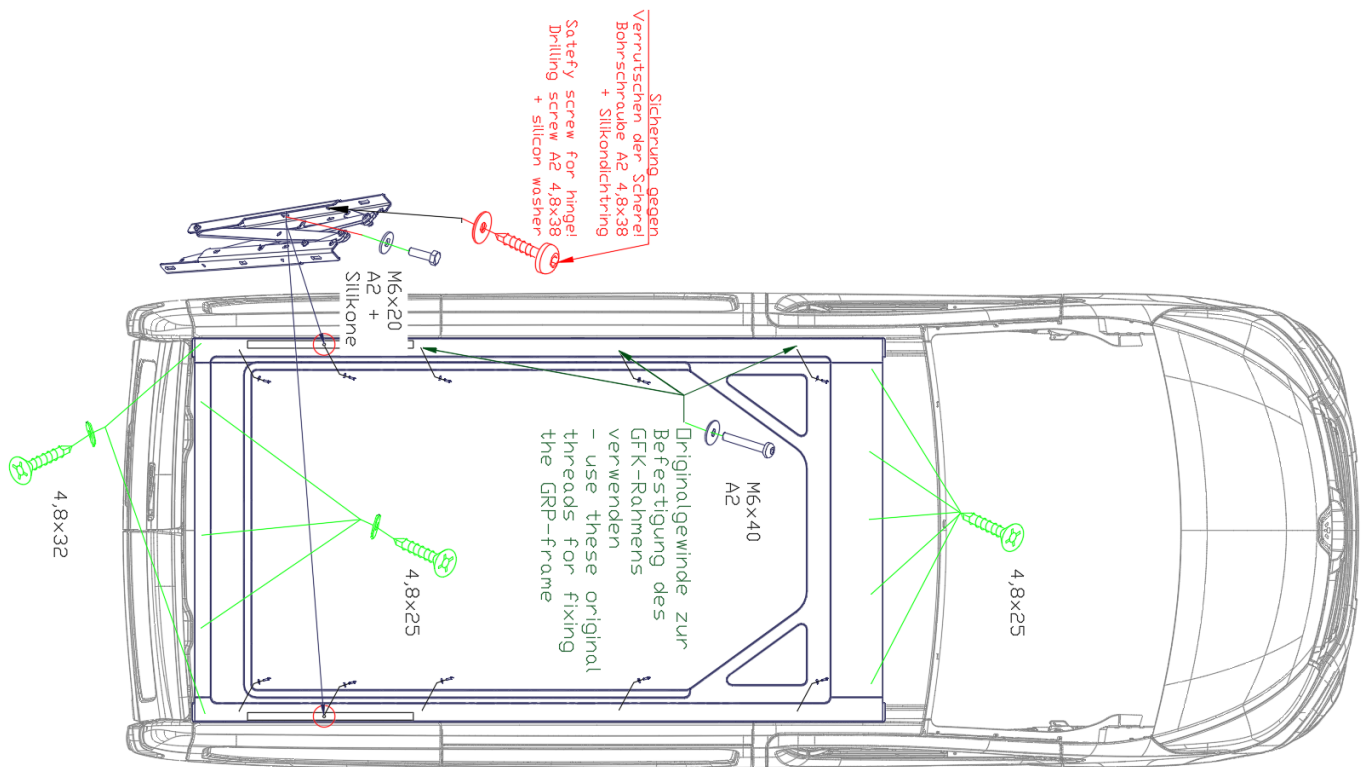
GFK-Rahmen Befestigungspunkte und Scherensicherung / GRP frame fixing points and hinge securing [A0003929]
